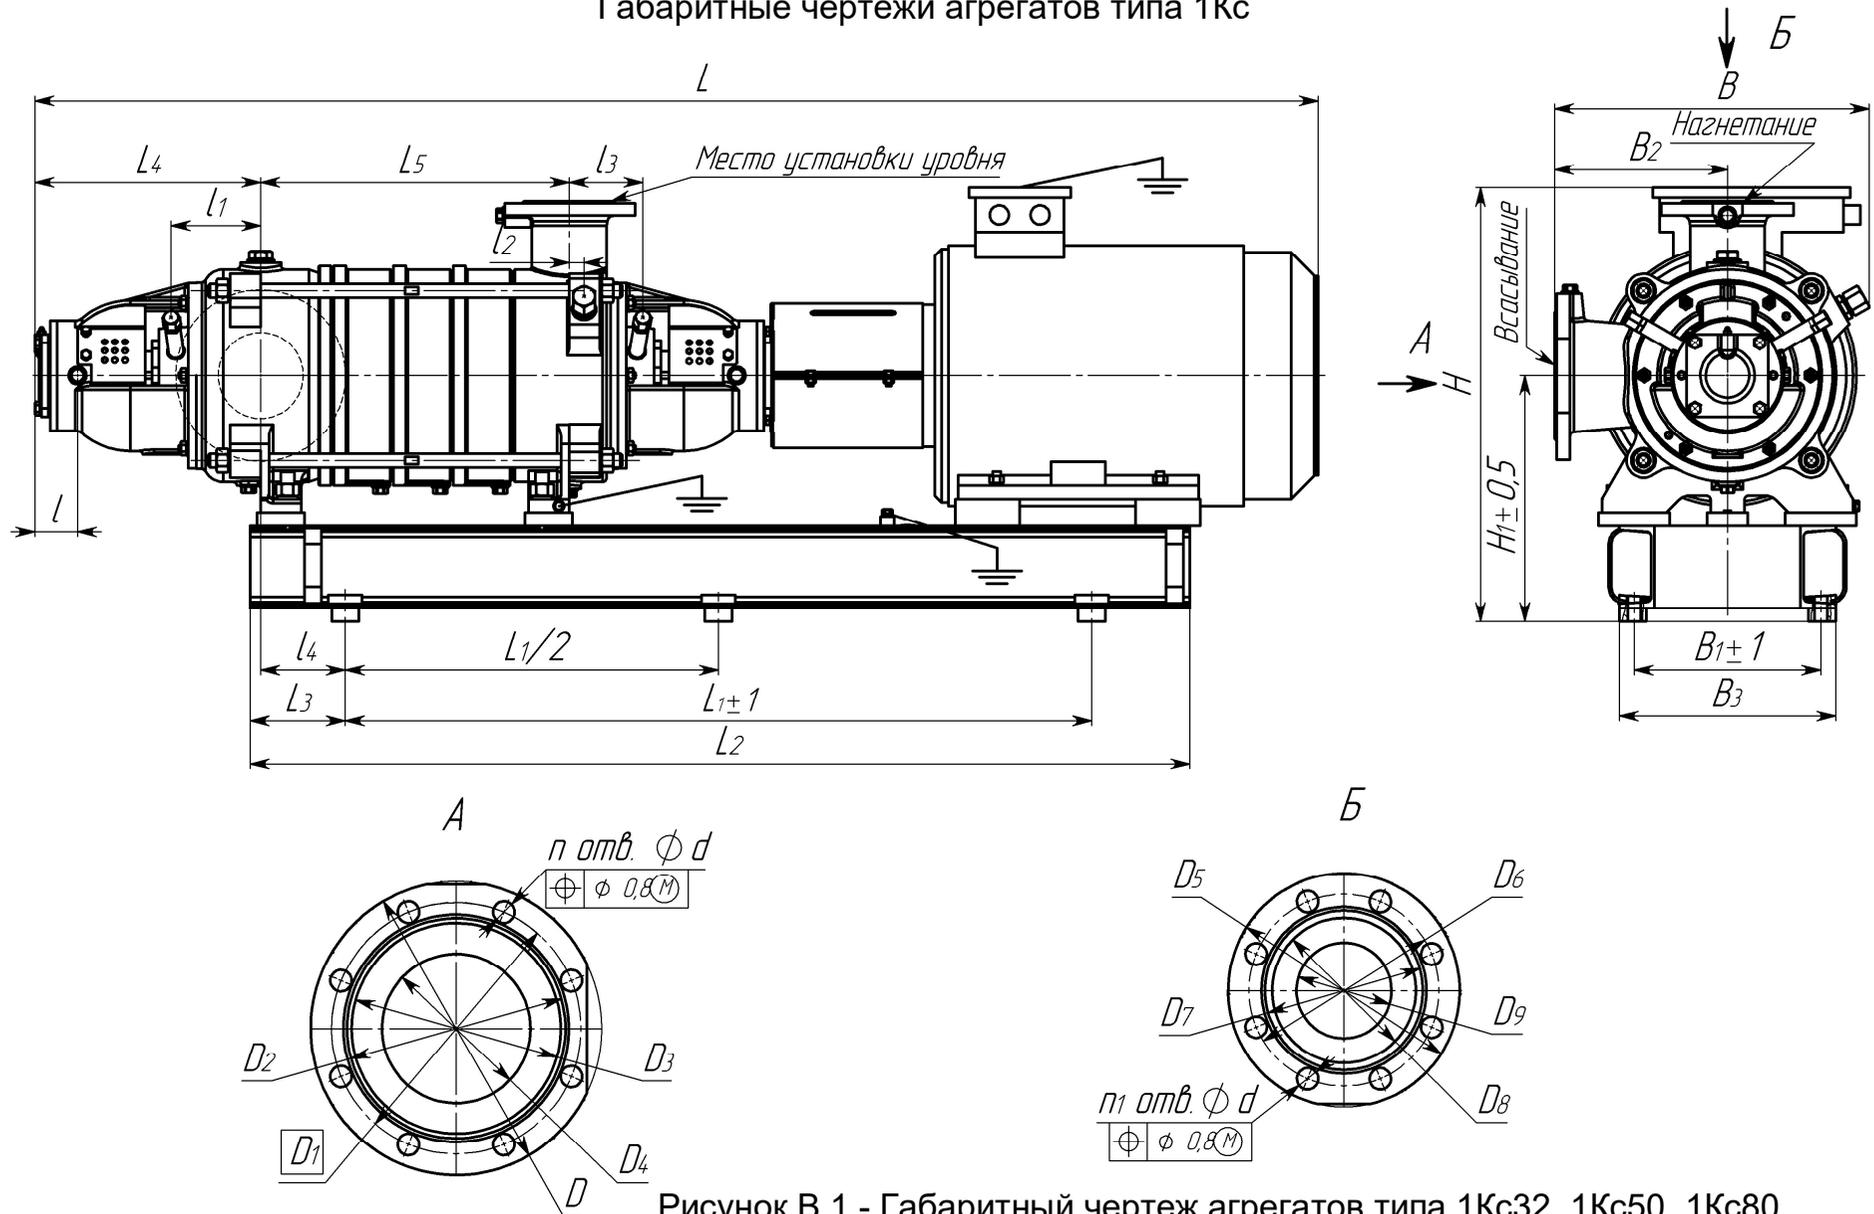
Габаритный чертеж агрегатов типа 1Кс32, 1Кс50, 1Кс80
